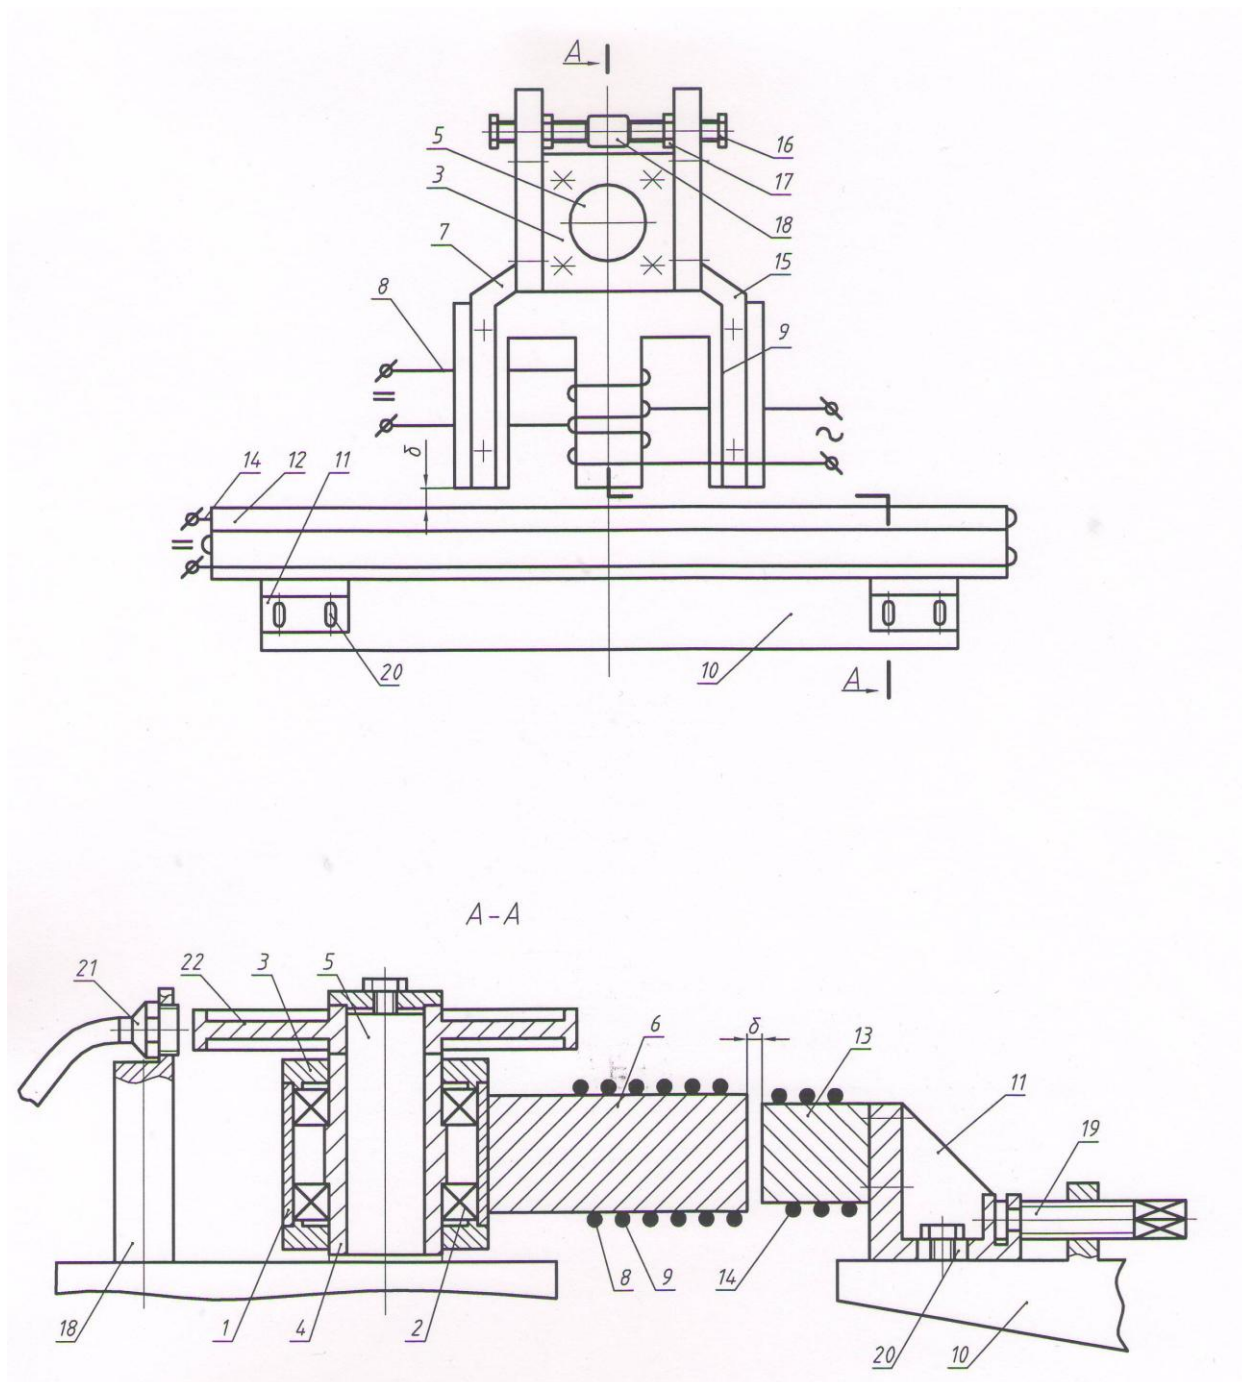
Нагрузочное устройство для испытаний фрезерных станков.
